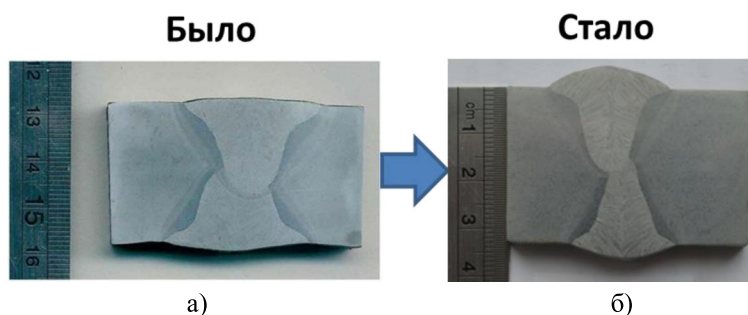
Макрошлифы продольных сварных швов труб типоразмером 1153x30,9 мм: а) стандартный режим; б) новый режим
